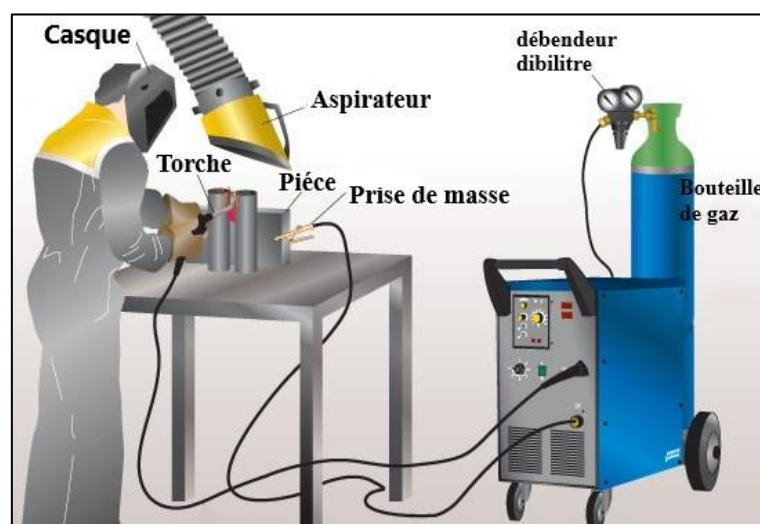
Les composants de soudage MIG/MAG. [8]
